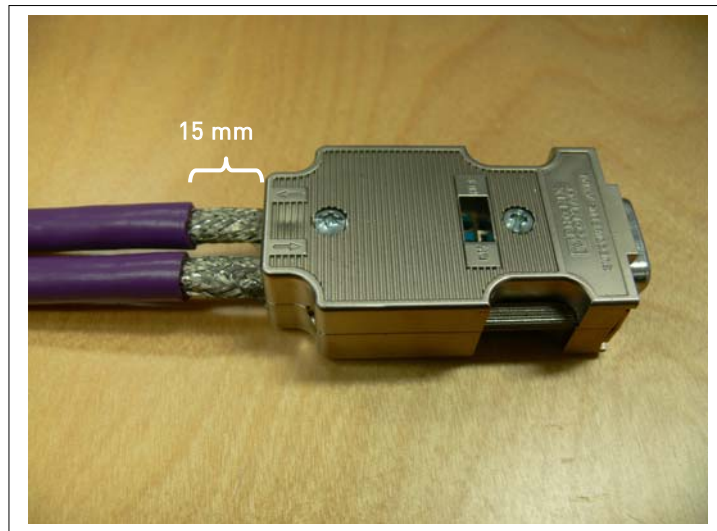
Den Mantel vom Kabel wie im Bild dargestellt entfernen
